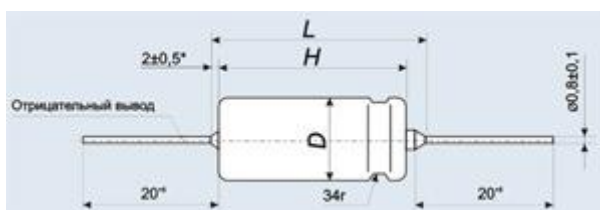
Габаритный чертеж корпуса оксидно-электрического алюминиевого конденсатора К50-29 (тип 2).
